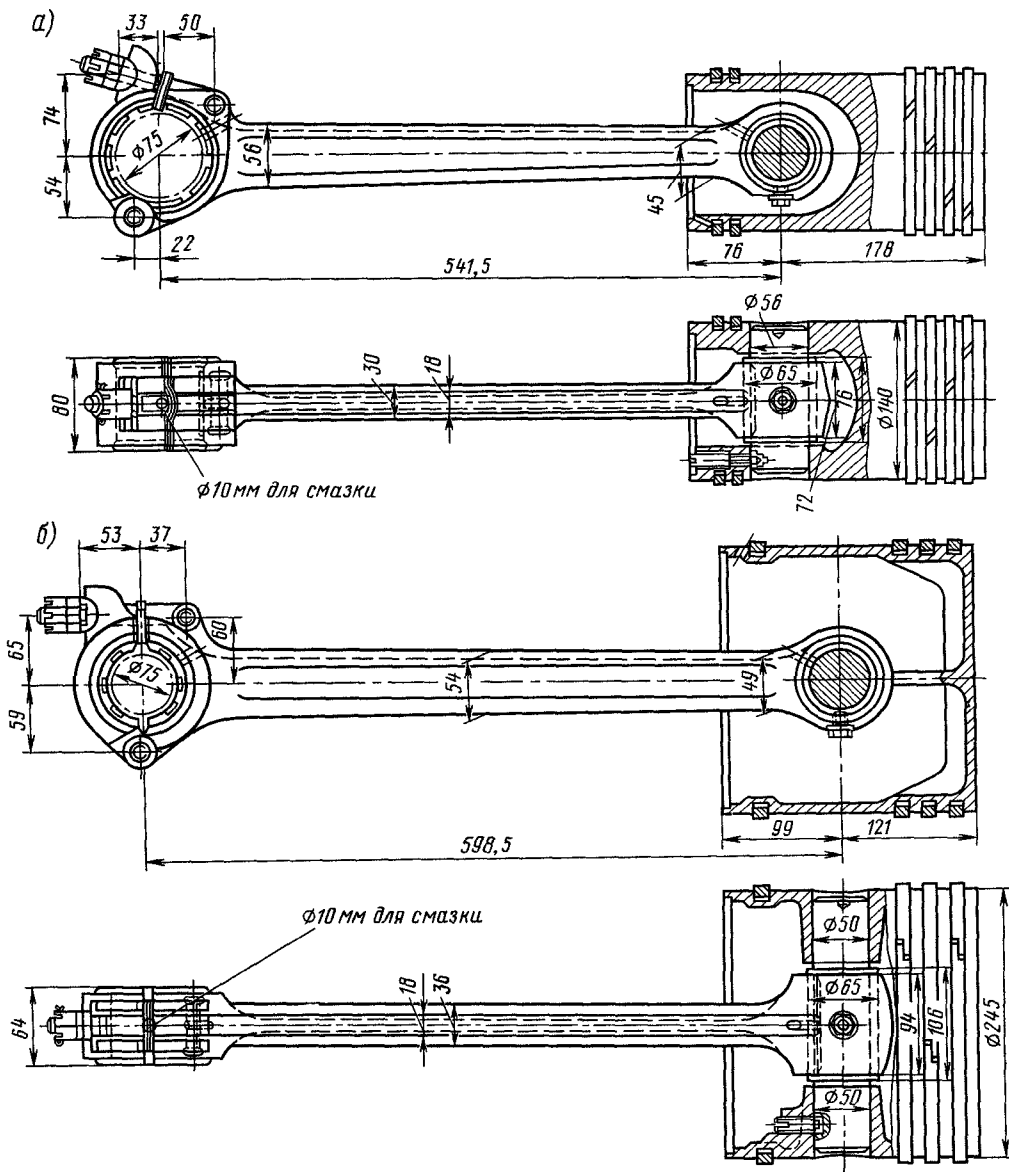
Шатуны компрессора Э-500 в сборе с поршнем.
